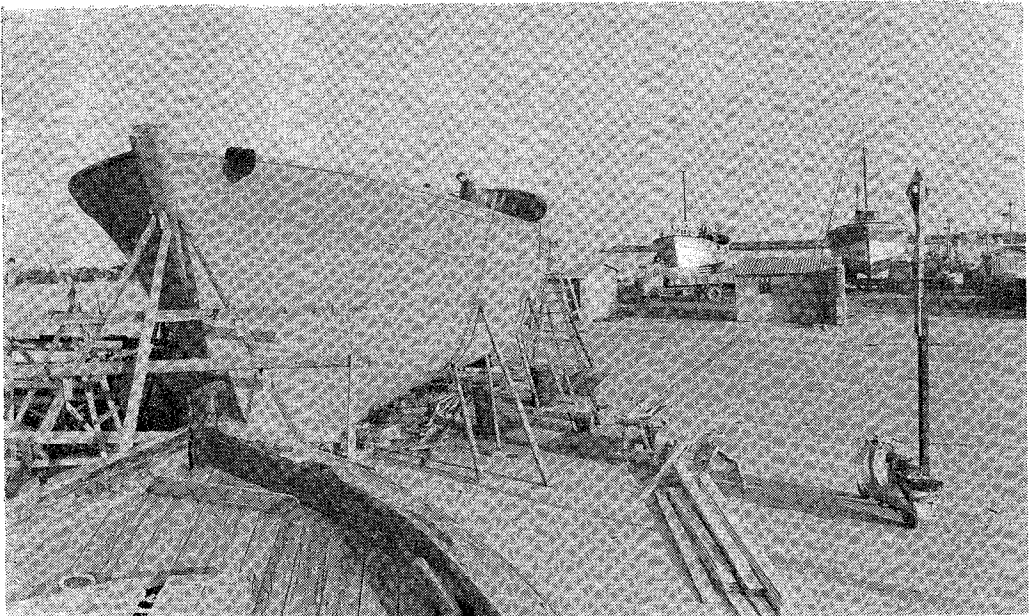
Una vista del varadero de Castellón. En primer plano, nuevas unidades en construcción.
